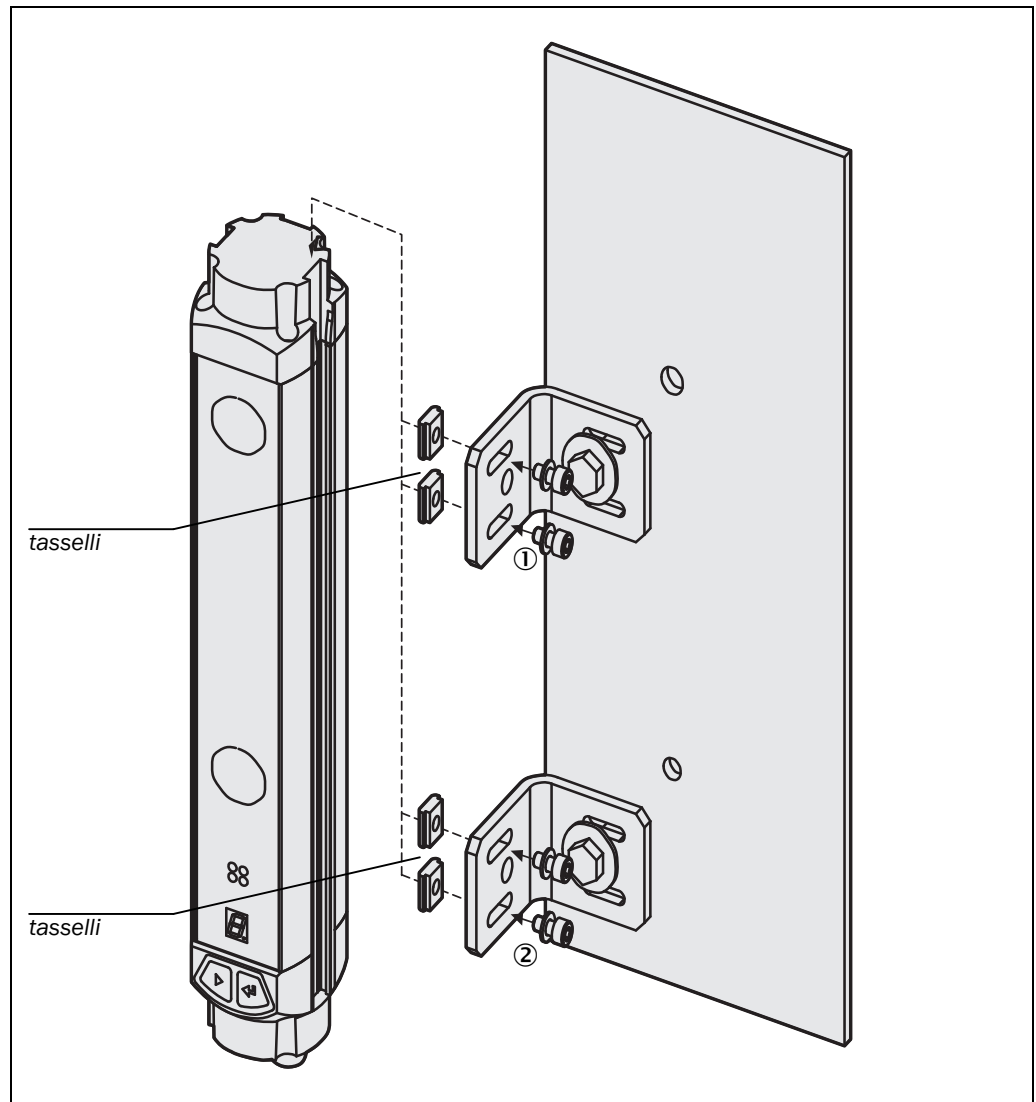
montaggio della M4000 con squadretta di fissaggio rigida
